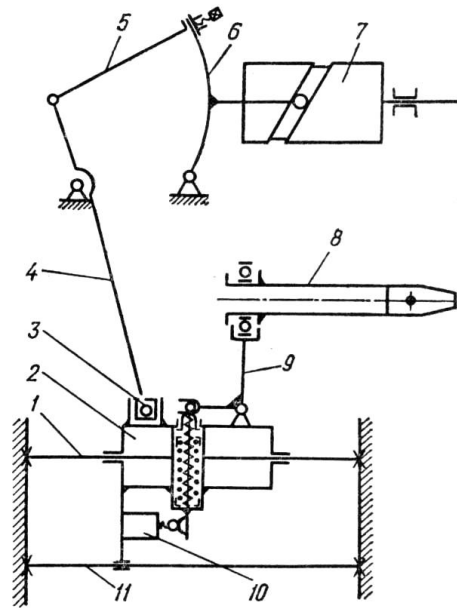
Типова схема механізму подачі прутка БТА
